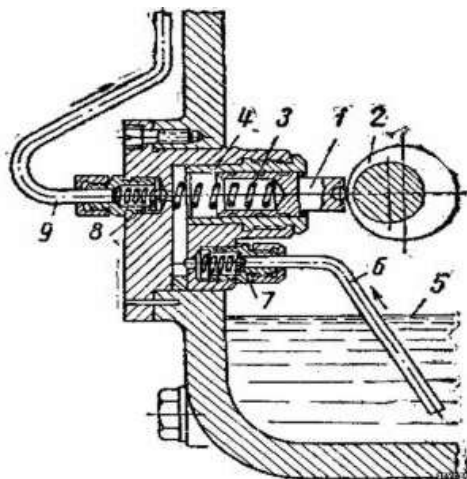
Плунжерный насос для циркуляционной смазки: 1 — плунжер; 2 — эксцентрик, насаженный на вал механизма; 3 — пружина, прижимающая плунжер к эксцентрику; 4 — цилиндр плунжера; 5 — маслосборник; 6 — всасывающий маслопровод; 7 и 8 — обратный шариковый клапан; 9 — нагнетательный маслопровод.
